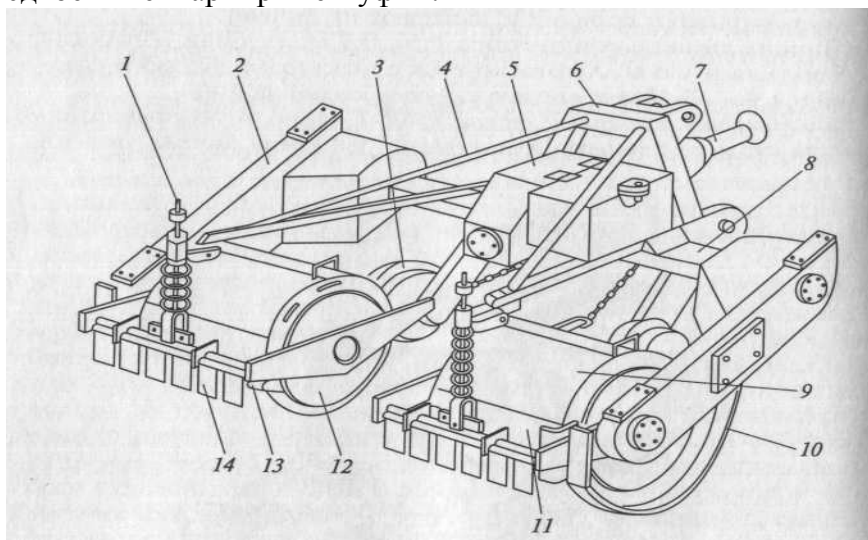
Культиватор фрезерный лесной КФЛ-1.4
